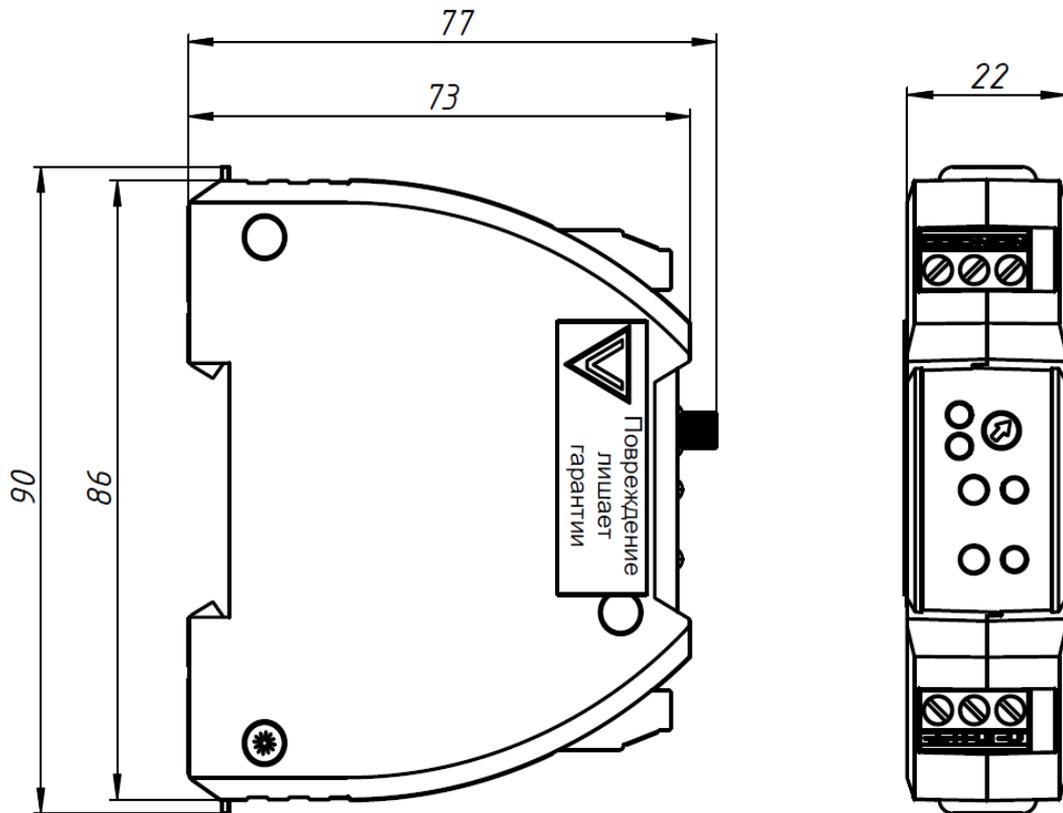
Внешний вид. Габаритный чертёж РКСИ-1001
